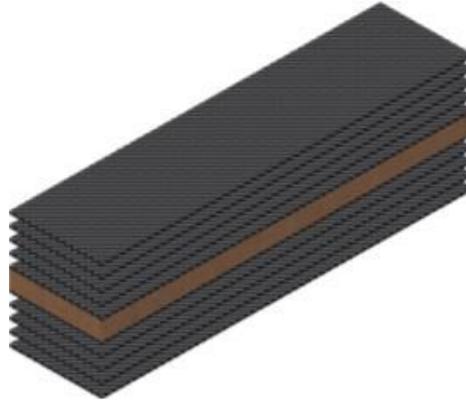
Dimensi pengujian *bending* standar ASTM D790 [7]
